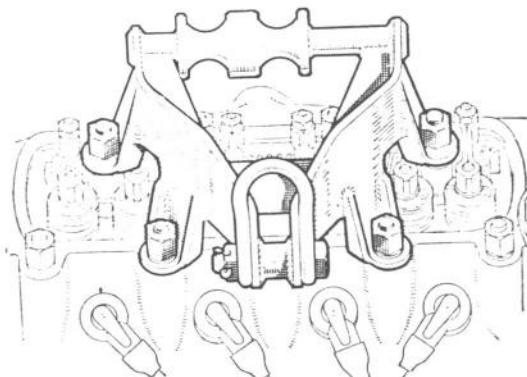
Util para levantamiento del motor, colocado en la culata después de retirar la tapa de balancines.
